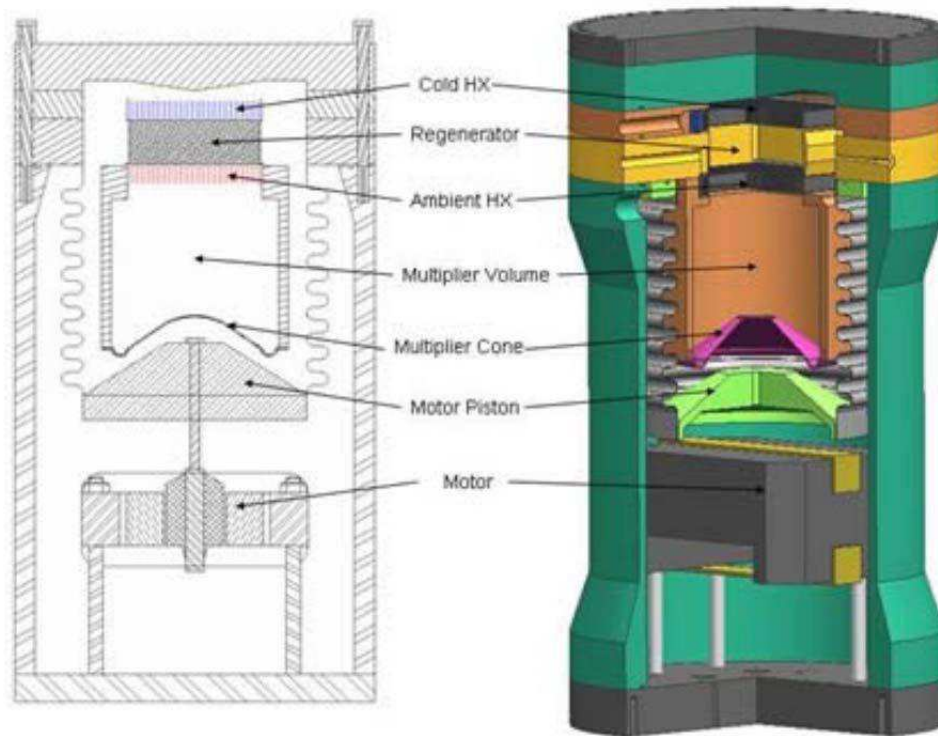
Congélateur thermoacoustique Ben & Jerry's (Pen State university)
